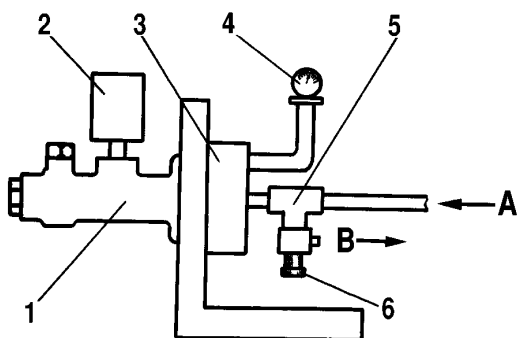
Dichtheitsprüfung des hinteren Dichtringes:
